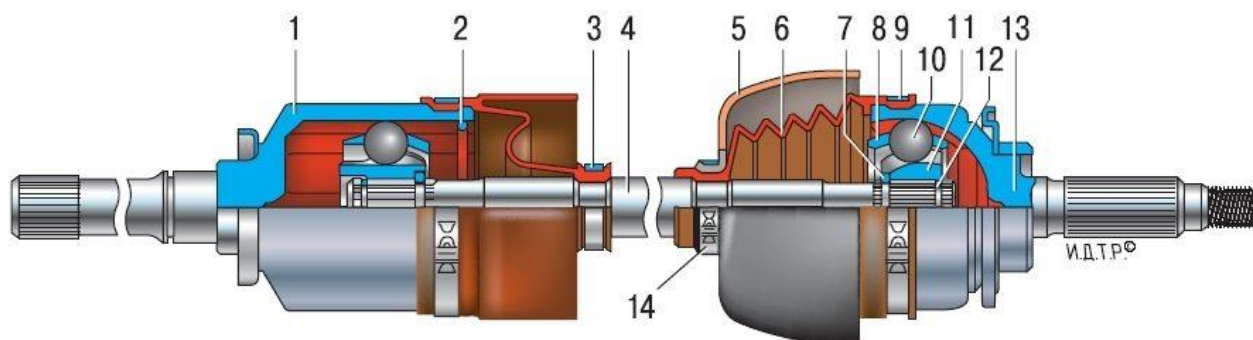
Привод переднего колеса Шеви Нива
